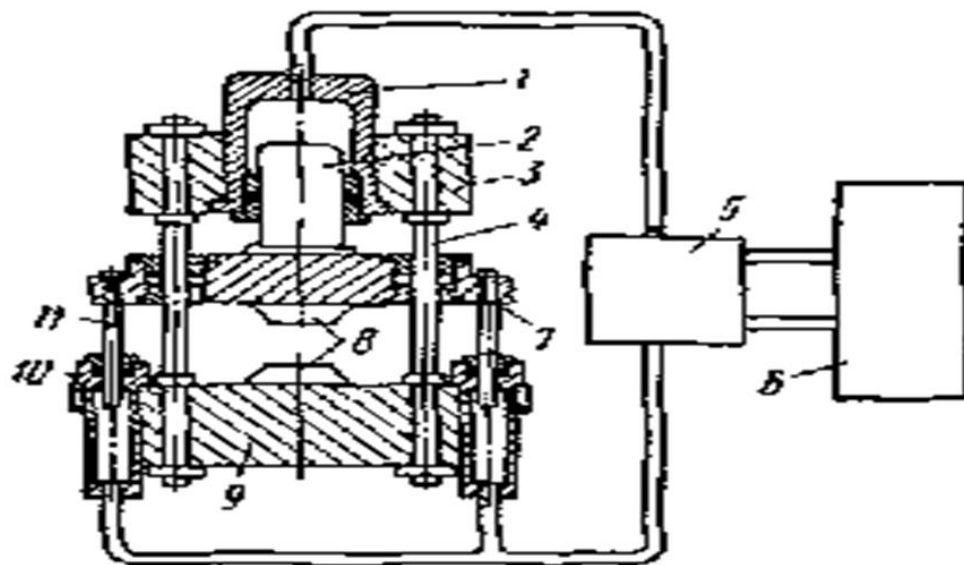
Схема ковочного гидравлического прессы: 1 – рабочий цилиндр; 2 – плунжер; 3 – неподвижная поперечина; 4 – колонны; 5 – система управления; 6 – привод; 7 – подвижная поперечина; 8 – бойки; 9 – неподвижная поперечина.
